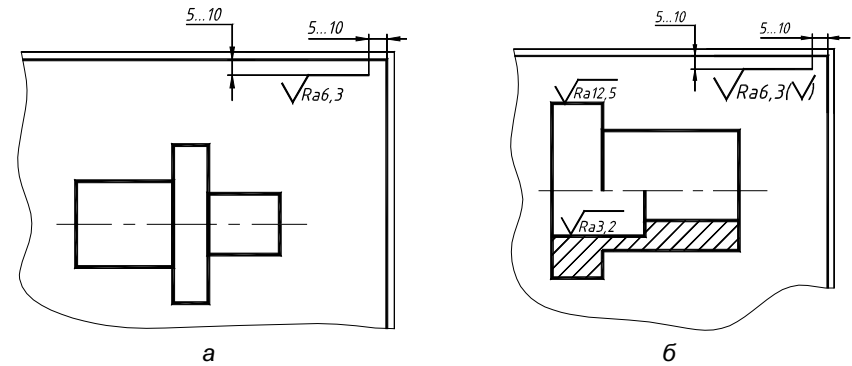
Обозначение шероховатости: а - одинаковой для всех поверхностей; б - часть поверхностей детали имеет одинаковую шероховатость
